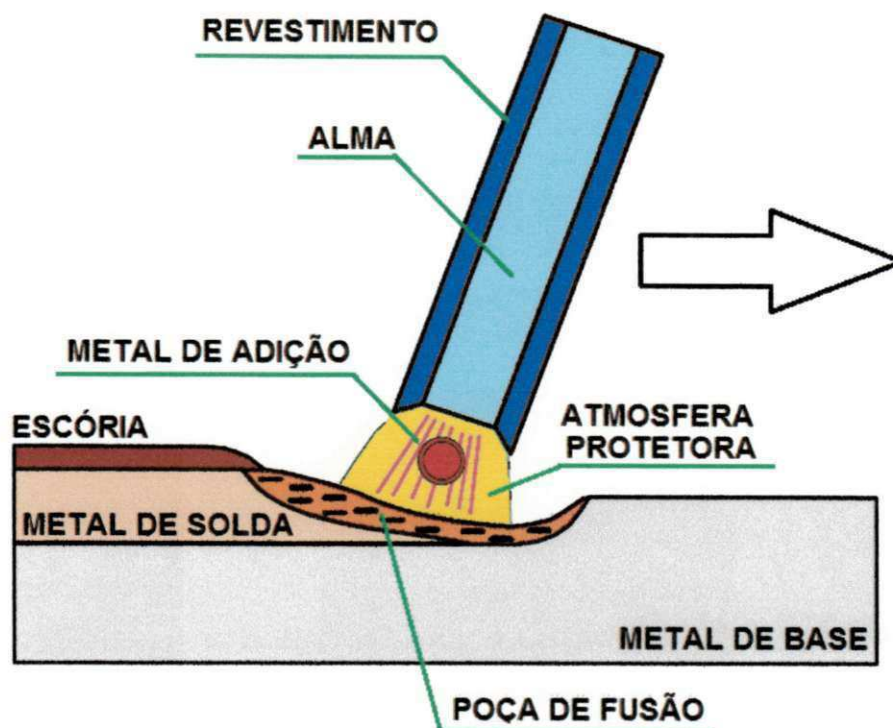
Processo de soldagem manual com eletrodo revestido adaptado de Marques et al. (2005).
